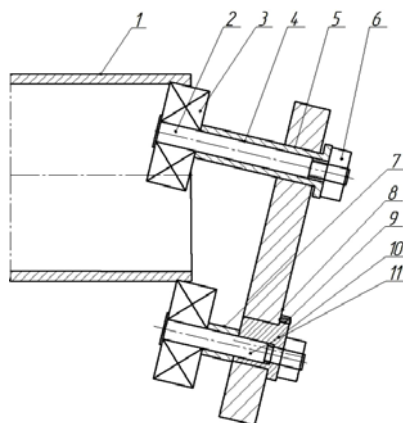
Устройство для отрезки трубчатых заготовок от цилиндрической трубы
